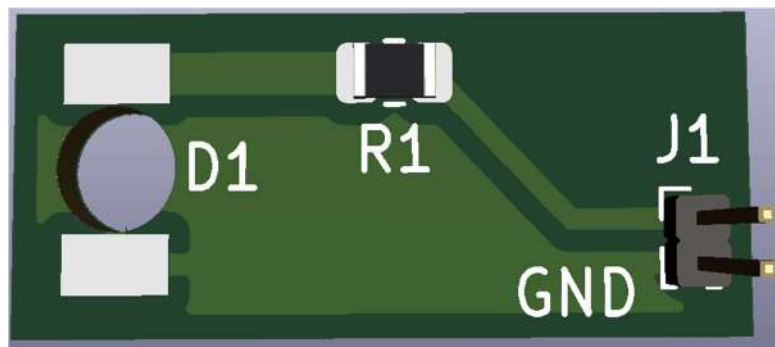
Visionado 3D placa circuito impreso de circuito de iluminación
